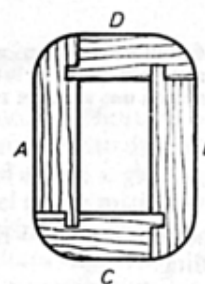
Sezione di albero in quattro pezzi con unione a dente e canale; il lato C corrisponde alla faccia poppiere rettilinea.
